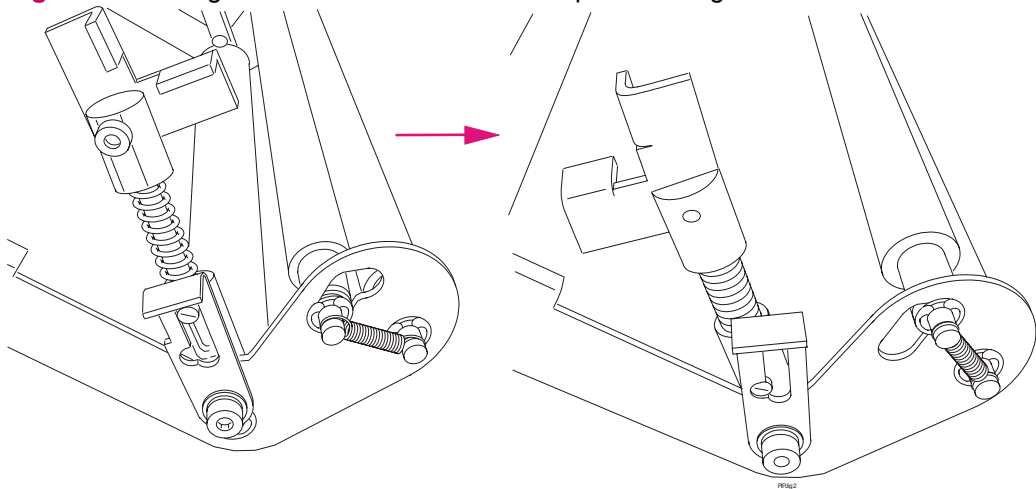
Dispositivo de instalación de la capa subyacente de la PIP
